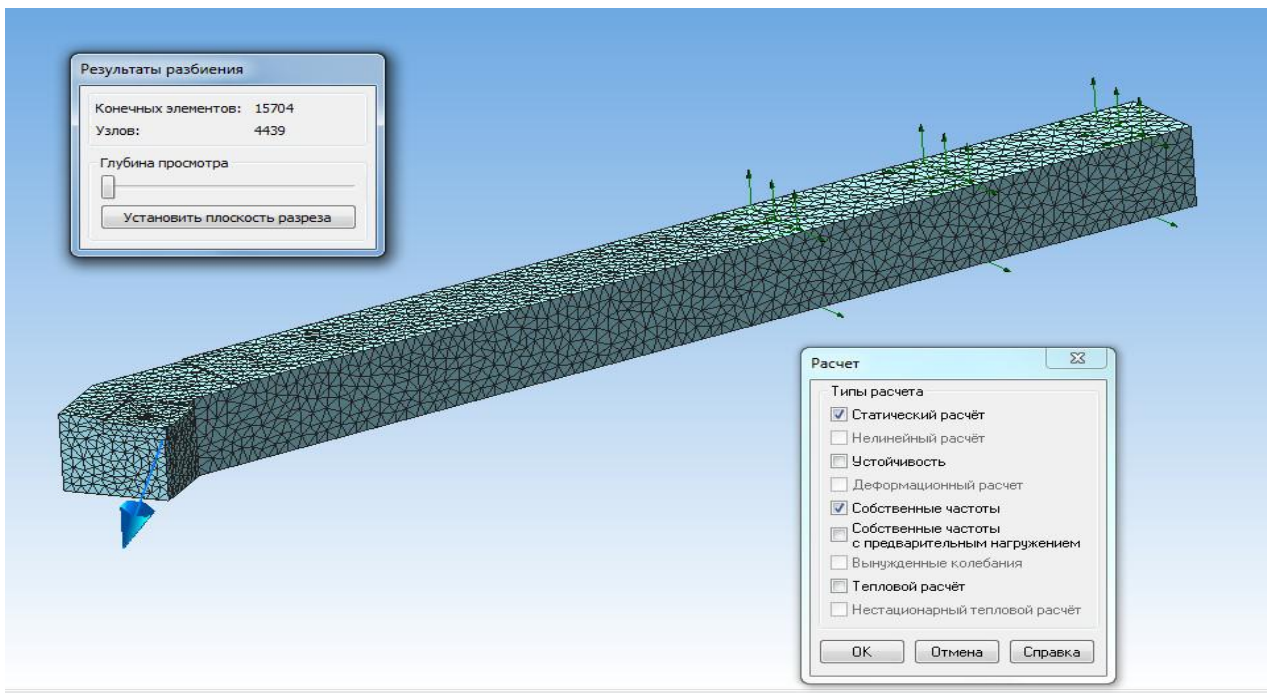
Конечно-элементная модель сборного расточного резца
